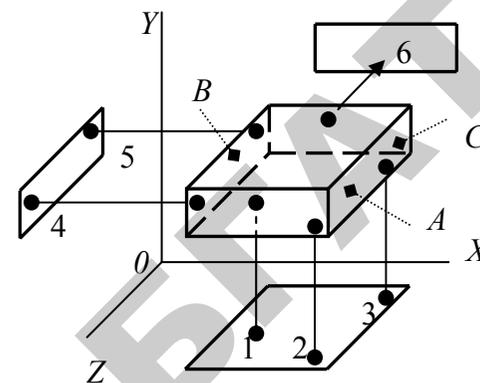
Базирующие поверхности и опорные точки призматического изделия
